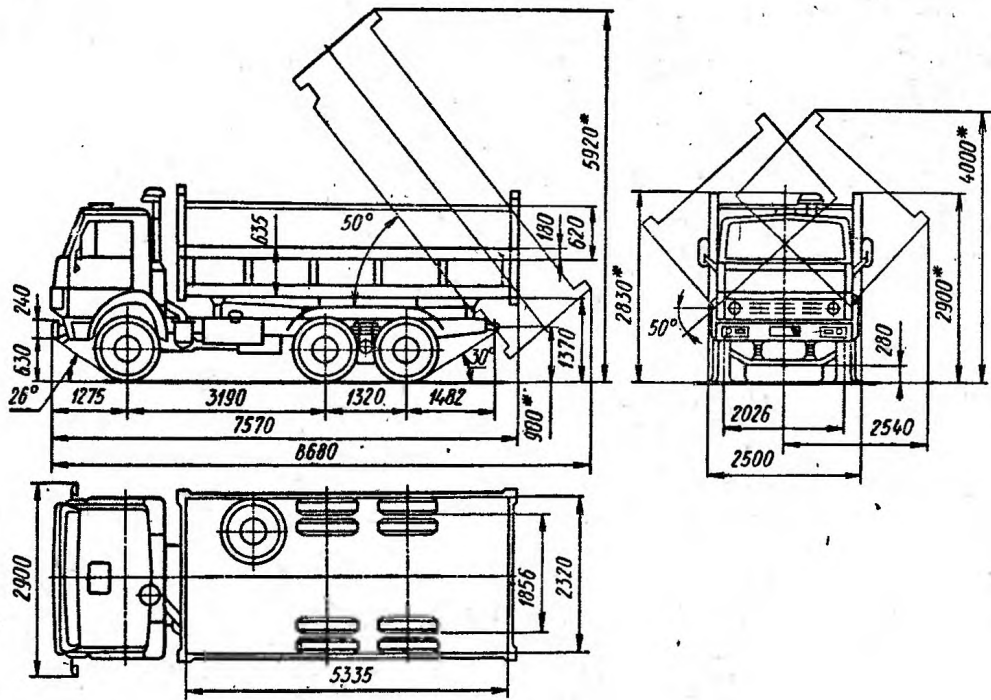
Габаритные размеры самосвала-тягача КамАЗ-55102
